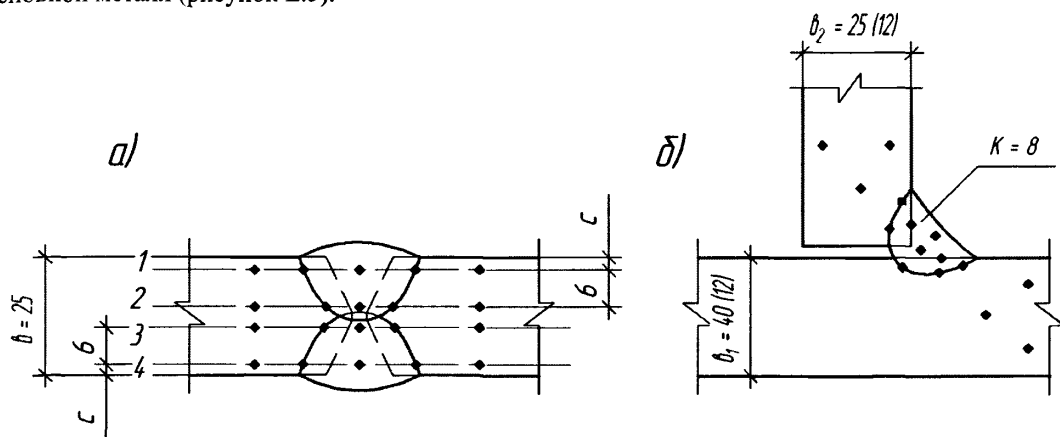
Образец для испытания металла шва толщиной 25 мм на ударный изгиб (КСУ)
